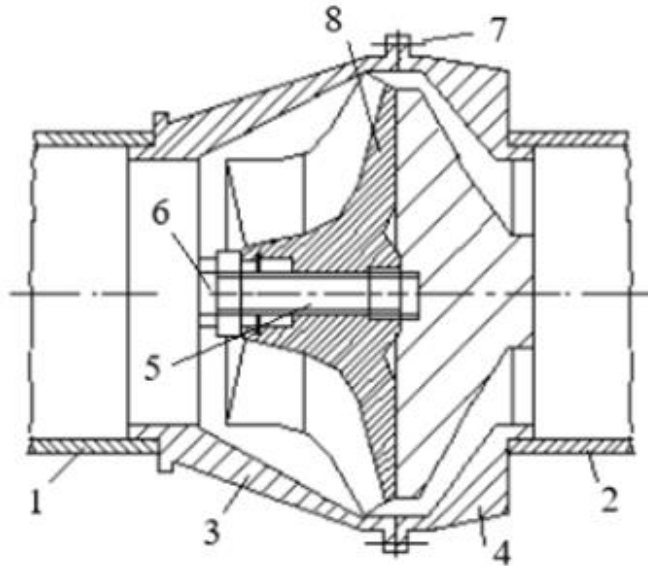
Общая схема базирования и закрепления заготовки в приспособление для обработки абразивным потоком
